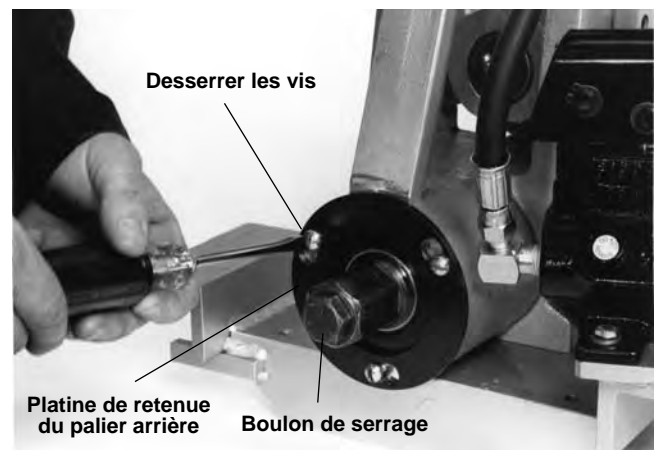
Desserrage du boulon de serrage et des vis 6-pans de la platine de retenue
